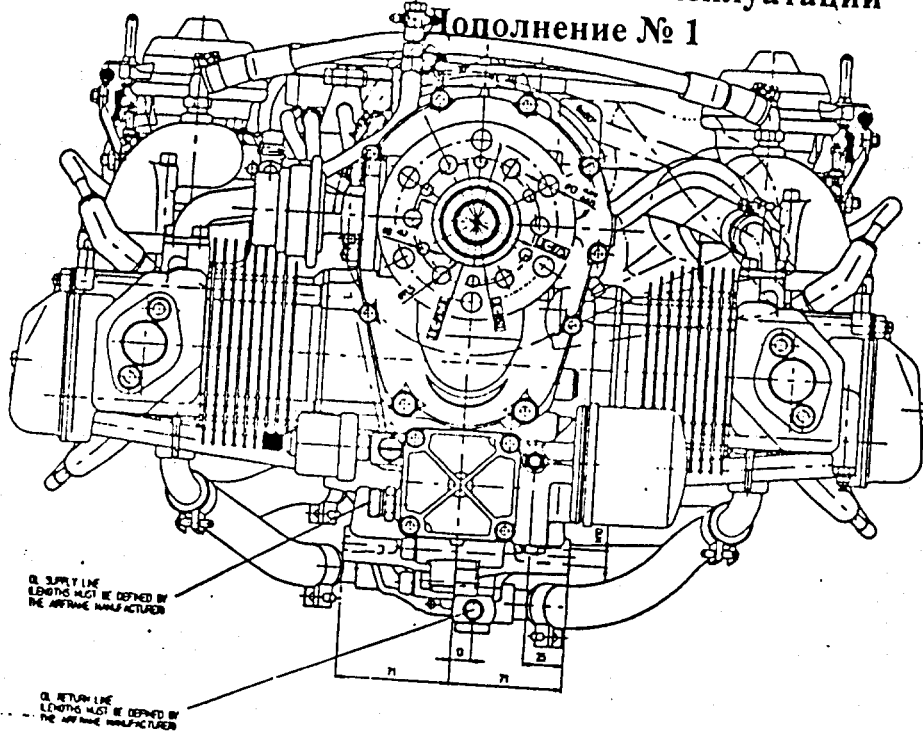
Общий вид двигателя "Rotax-912ULS2"
